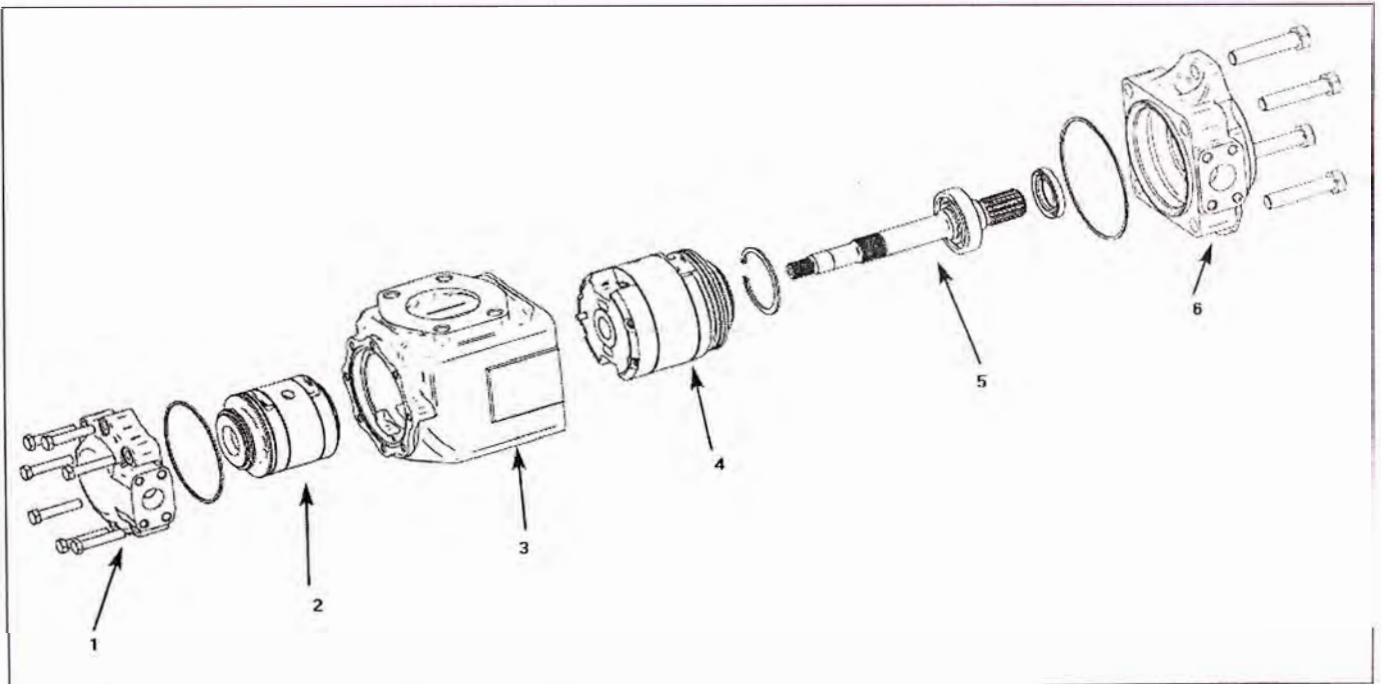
Despiece de Bomba Oleo Hidráulica: (1) Tapa posterior,(2) Cartucho,(3) Carcasa, (4) Cartucho, (5) Eje,(6) Tapa delantera.
